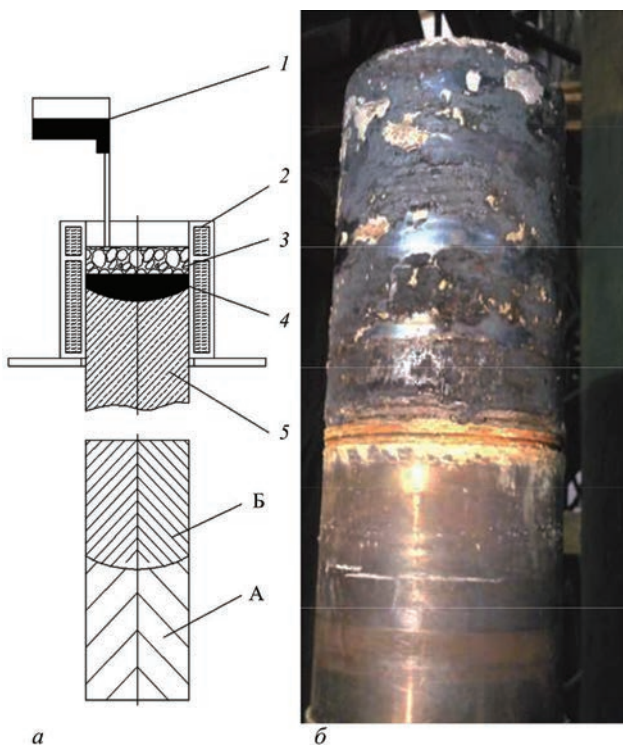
Схема виготовлення композитного зливка способом ЕШП РМ (а) і загальний вигляд зливка (б): 1 — пристрій для подавання рідкого металу; 2 — струмопідвідний кристалізатор; 3 — шлакова ванна; 4 — металеві ванна, сталь 38ХНЗМ-ФА (Б); 5 — вихідна заготовка, сталь 12Х13 (А)
